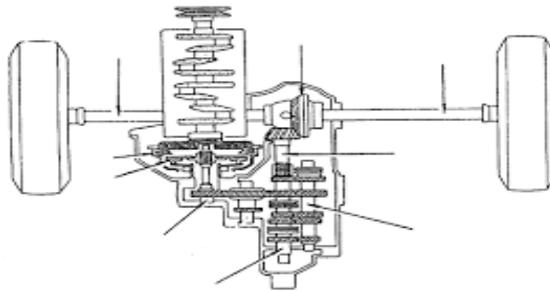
8 Transmisi penggerak roda belakang motor belakang
